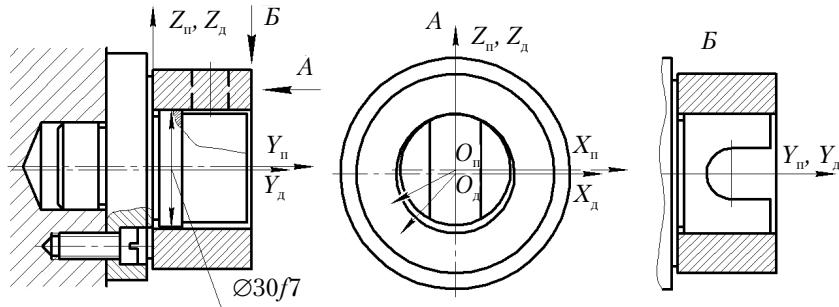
Разработка конструкции установочных элементов и схема установки
